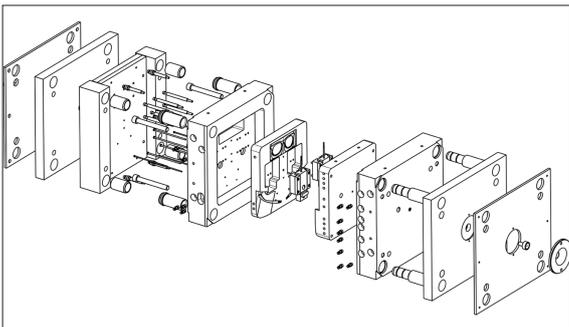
Explosionsdarstellung des Spritzgiesswerkzeuges
